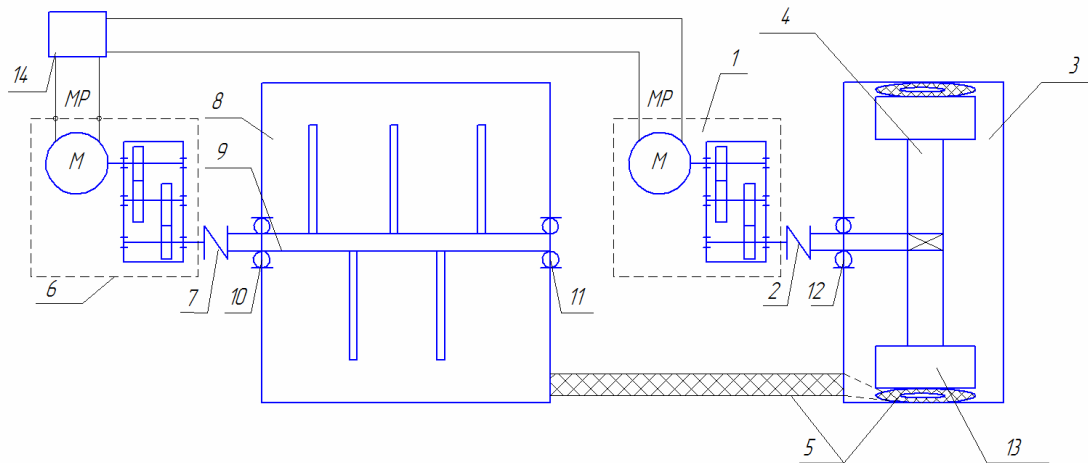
Кінематична схема безпоршневого універсального бетононасоса з механічним приводом:
